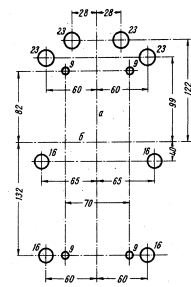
Сверление отверстий для установки на изоляционных плитах контакторов типа КТИ 523 и КТИ 543 с задним присоединением
